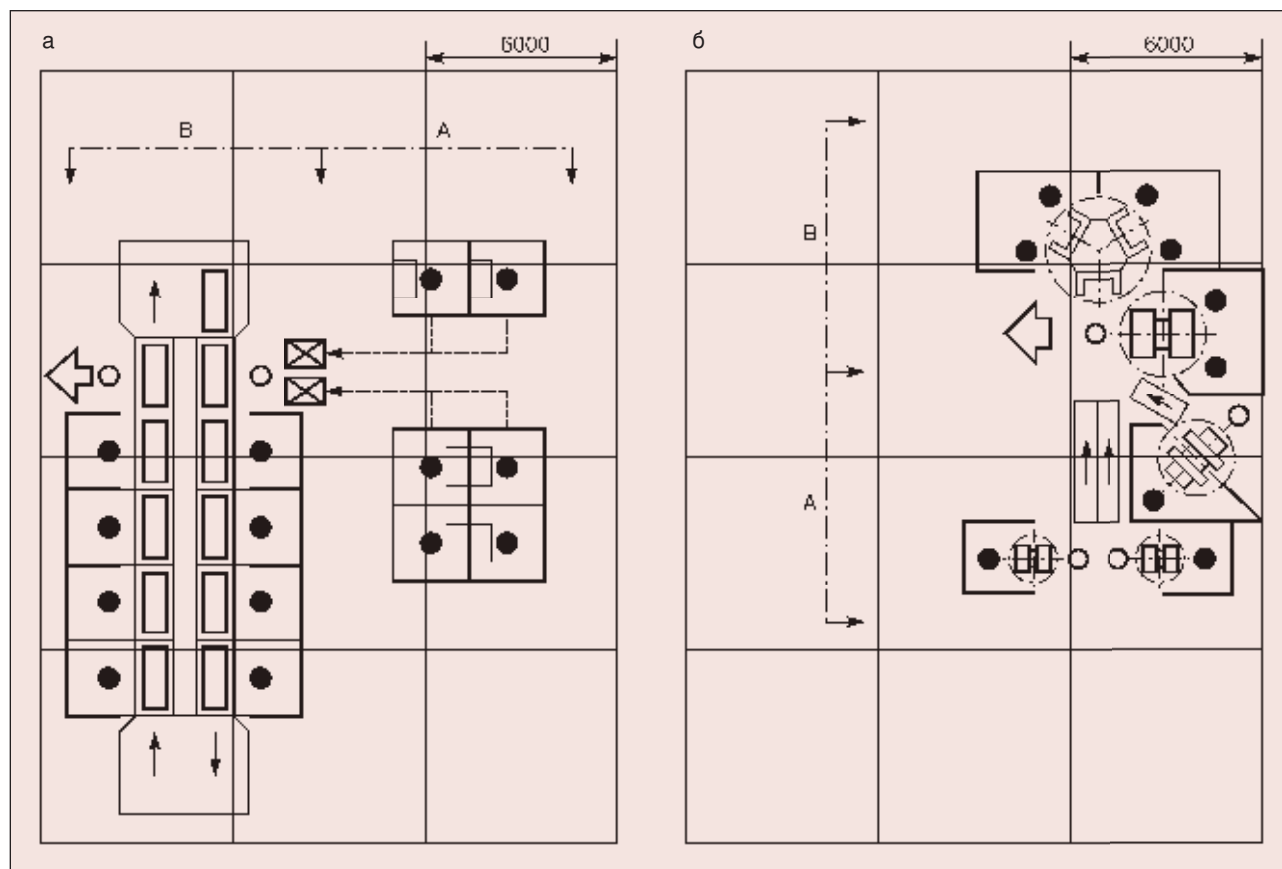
Технологическая схема сварки балки задней подвески автомобиля «Lanos»: а — действующая схема; б — альтернативная схема
